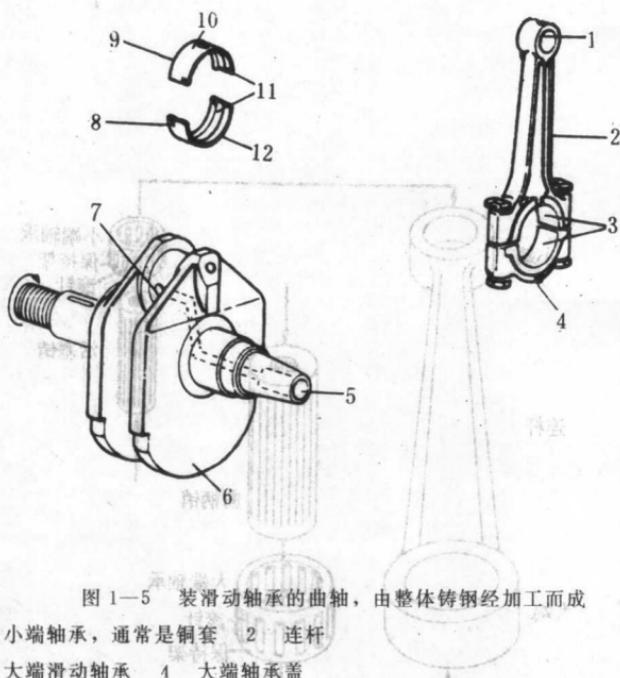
5 装滑动轴承的曲轴，由整体铸钢经加工而成
